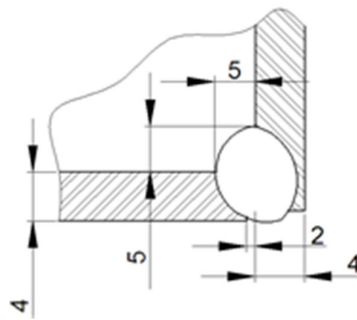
Схема зварного з'єднання У2 за ГОСТ 14771-76
